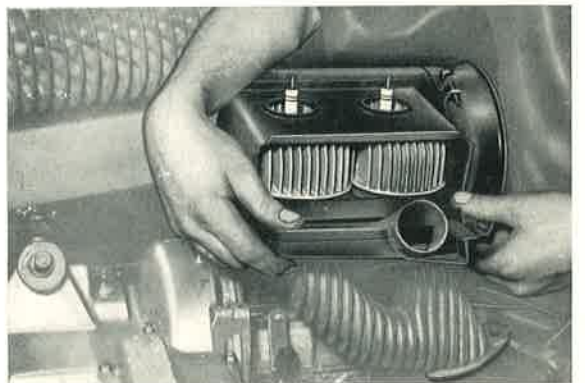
Das Oberblech des Heizungsgehäuses wird unter die Querrippe des Zyl.-Kopfes eingeschoben.
